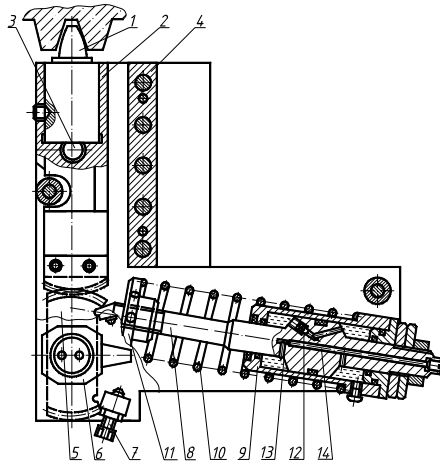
Устройство для обкатывания роликами клиноременных шкивов
